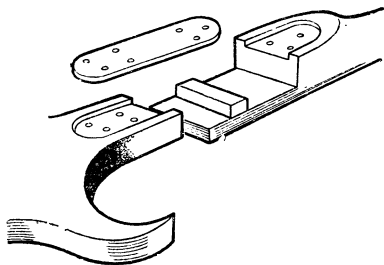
Способ крепления грифа к корпусу гитары.
